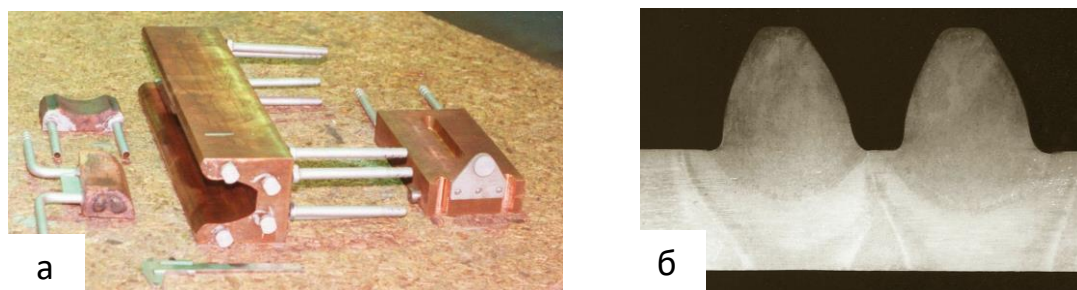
Внешний вид водоохлаждаемого формирующего устройства для восстановления зубьев шестерен  $m = 36$ ,  $z = 13$  (а) и поперечный макрошлиф зубьев, наплавленных без последующей механической обработки (б).
